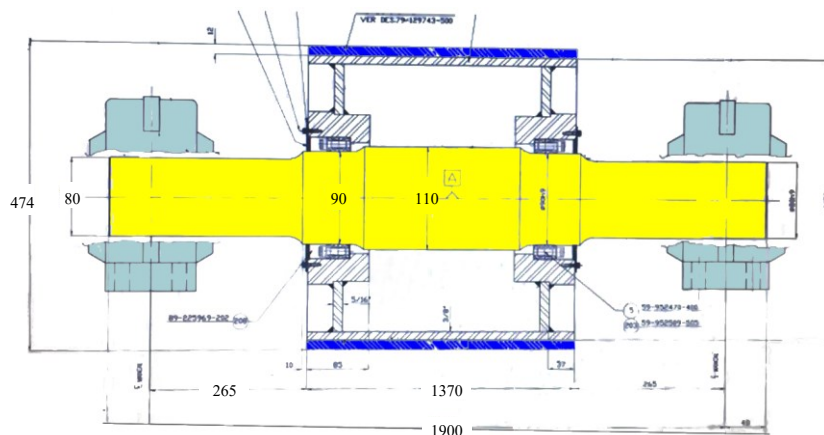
Projeto do tambor – Detalhe das principais dimensões (em mm).
